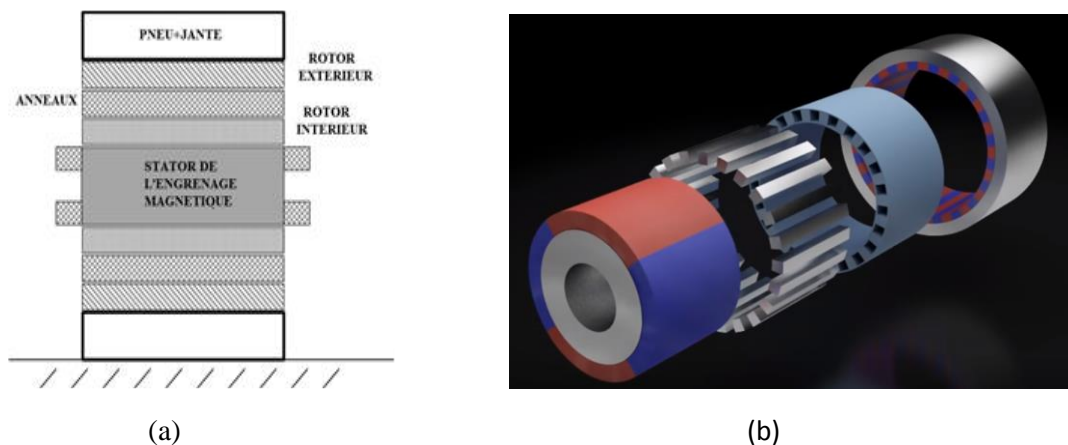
Engrenage magnétique (a)engrenage dans l'axe de la roue (b) ensembles des éléments fondamentaux
